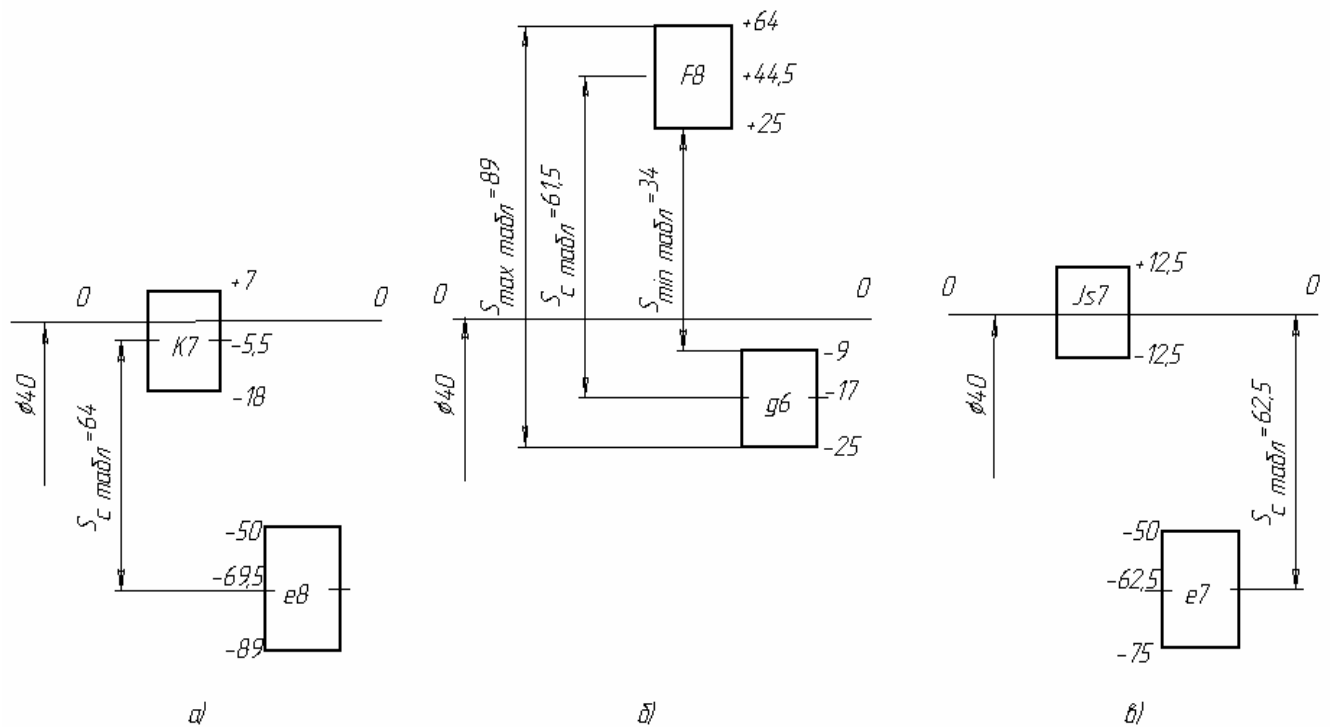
Схема расположения полей допусков вала и подшипника при комбинированных посадках
